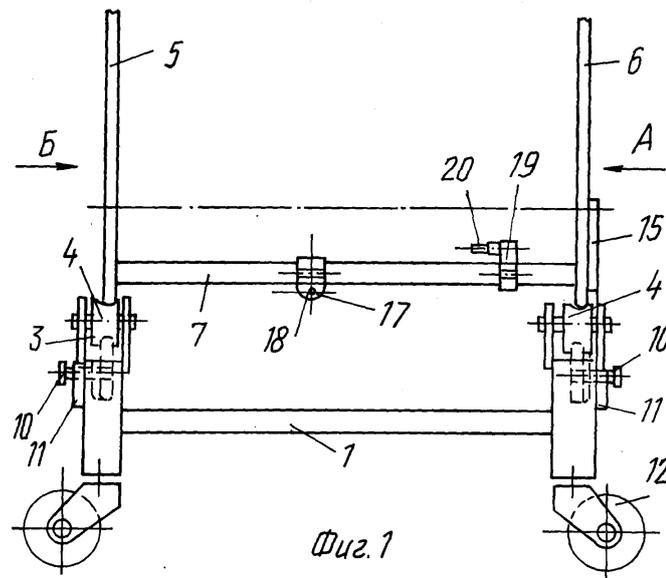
Стенд для разборки коробок передач по а.с. № 2127424
